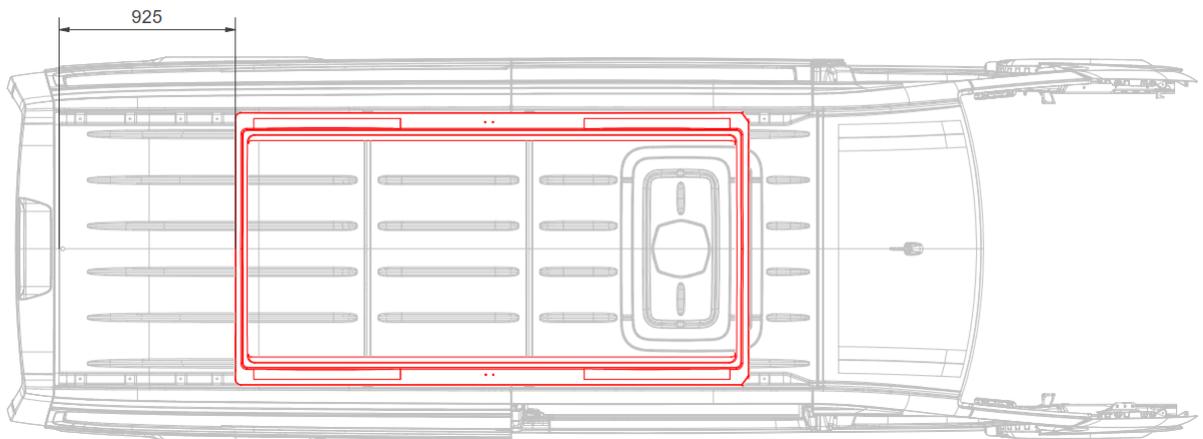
VW Crafter L4H3 (L = 6836 mm) [G0002143-001]
